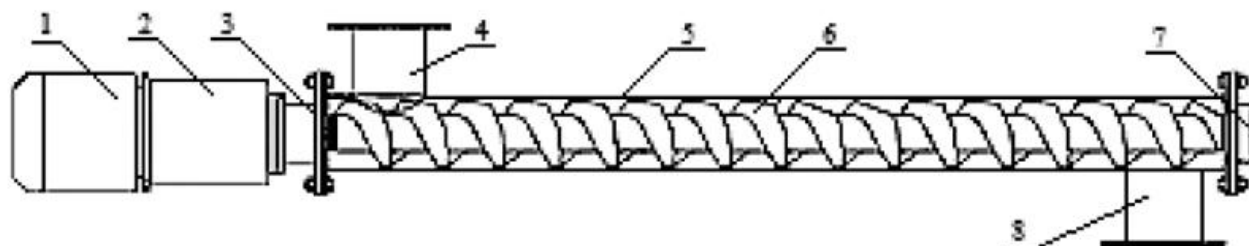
Винтовой конвейер. 1 – электродвигатель; 2 – редуктор; 3,7 – подшипниковые опоры; 4 – загрузочный люк; 5 – корпус; 6 – винт (шнек); 8 – разгрузочный люк.
